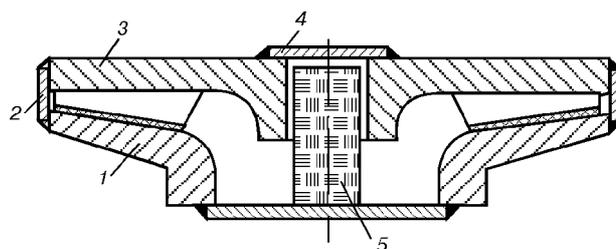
Схема процесса автовакуумной пайки рабочего колеса: 1 — диск; 2 — бандаж; 3 — диск с лопатками; 4 — технологическая заглушка; 5 — патрон с сорбентом и активатором
